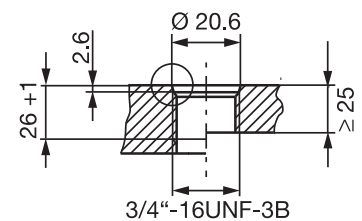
Einschraubloch für die Montage des BTL mit O-Ring
